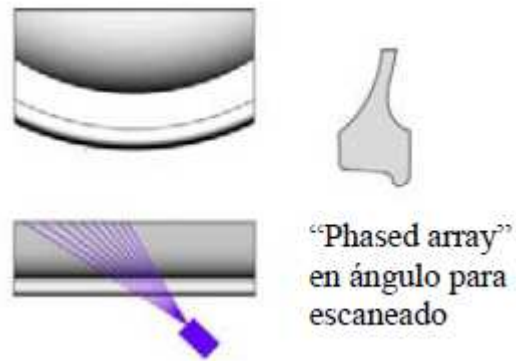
Inspección en busca de grietas térmicas en la zona exterior
